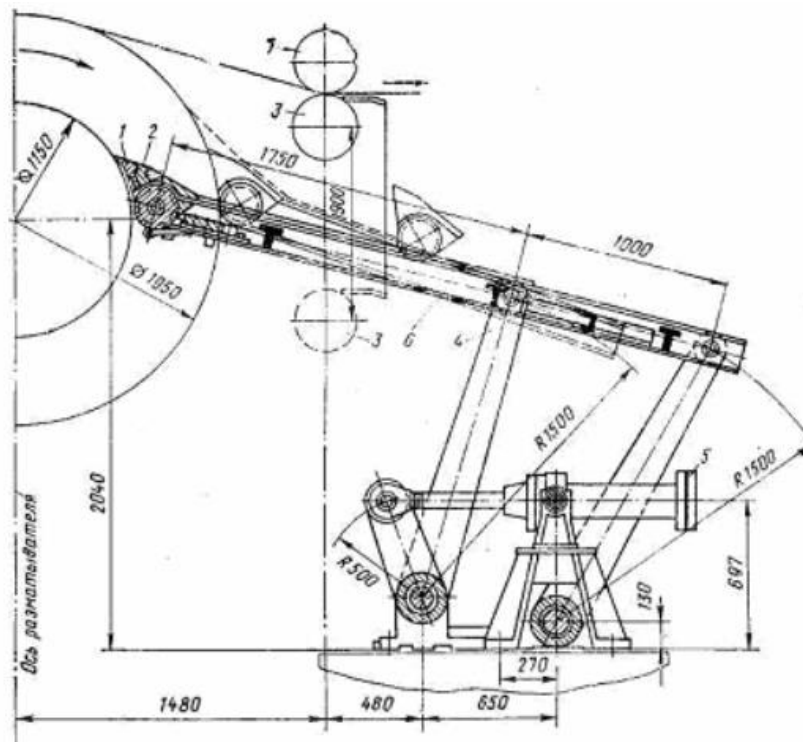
Скребковий відгинач кінця смуги: 1-скребок; 2 – головка; 3 – натискний рухомий ролик; 4 – важільно-паралогорамний механізм; 5 – гідроциліндр; 6 – важільна рама; 7 – приводний ролик
